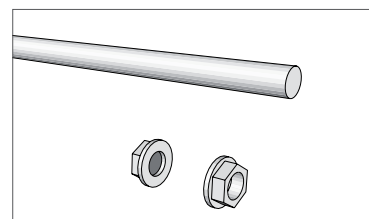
Pręt stabilizujący w lekkiej konstrukcji stropowej
